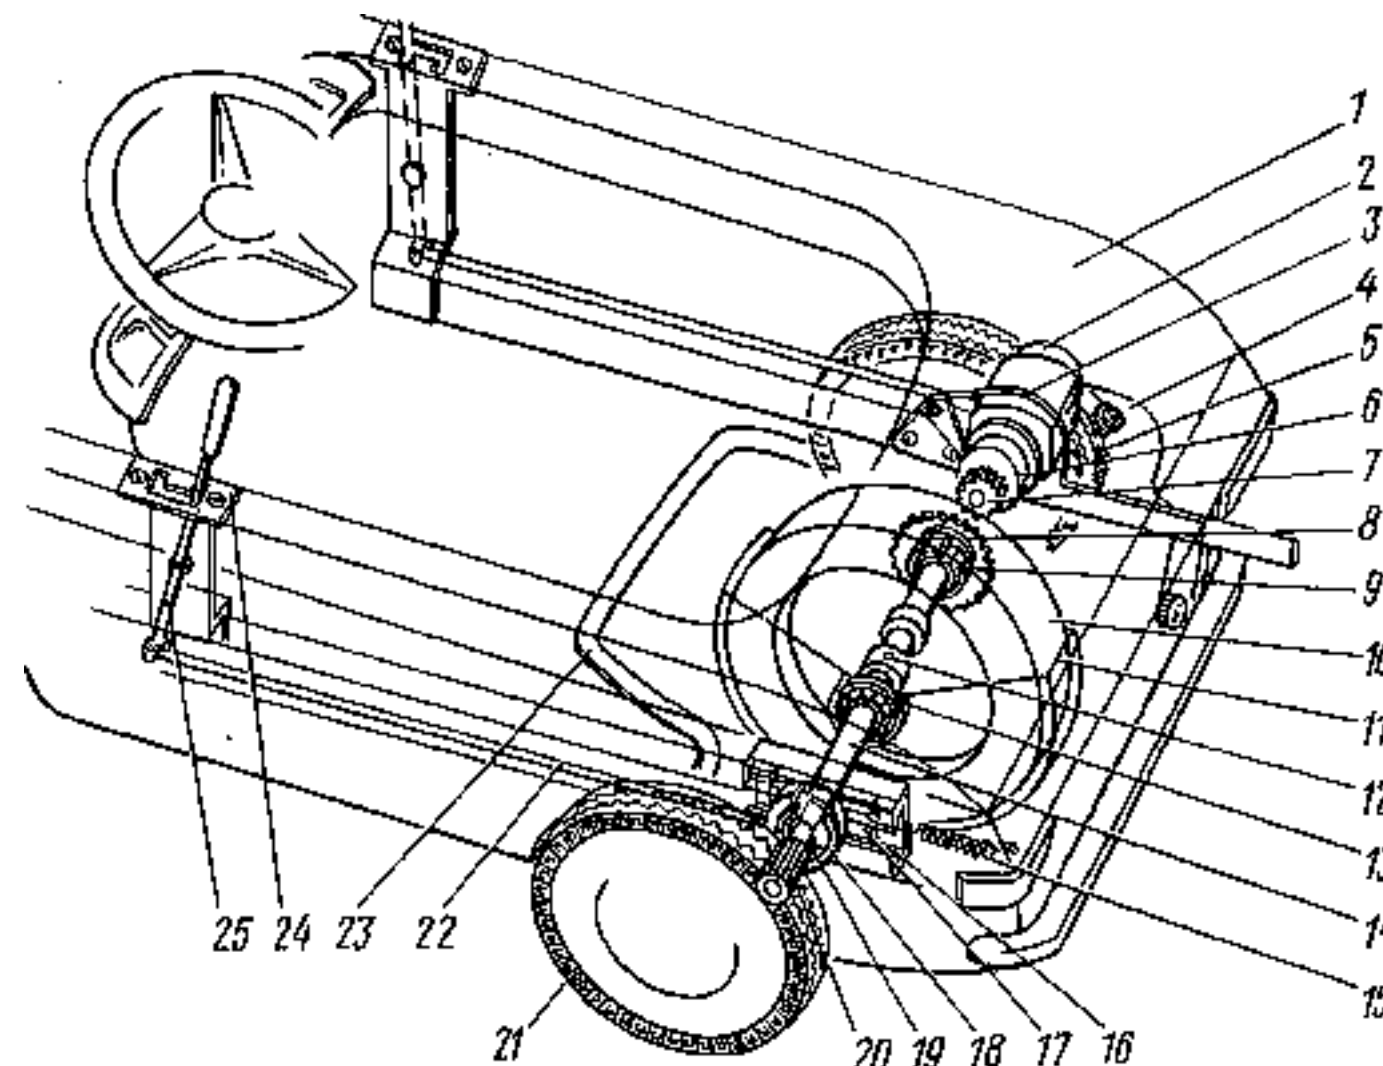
Схема привода автомобиля с маховичным двигателем:
